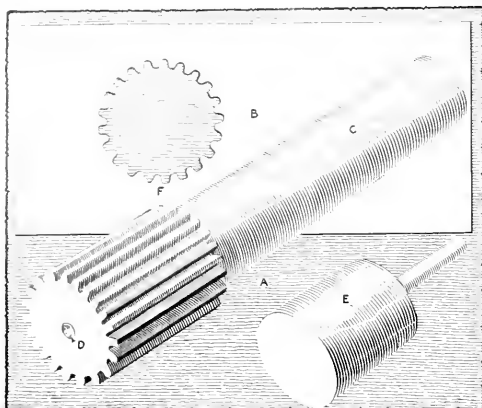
CORTADOR DE RUEDAS DENTADAS
